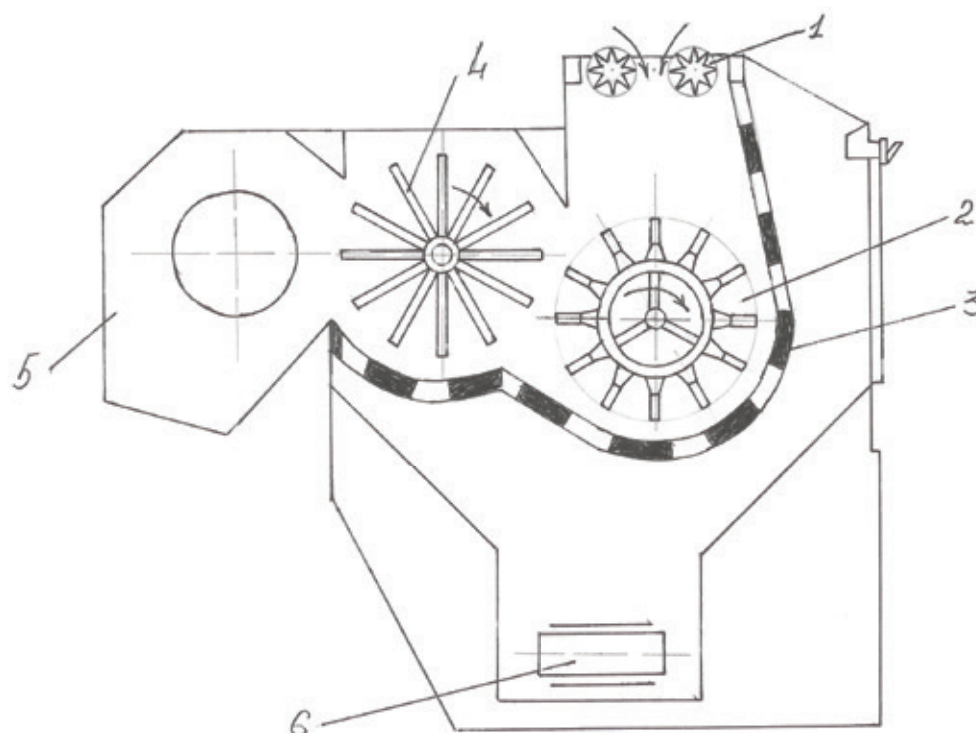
Схема предлагаемого питателя: 1-питающие валики; 2-колковый барабан; 3-сетка; 4-выпускной барабан (шпагатоуловитель; 5-лоток для подачи хлопка-сырца в рабочую камеру джина; 6-транспортер для удаления сорных примесей
